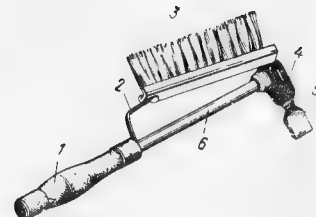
1 — ручка; 2 — кронштейн; 3 — пучок; 4 — головка; 5 — зубило сменное; 6 — стержень
